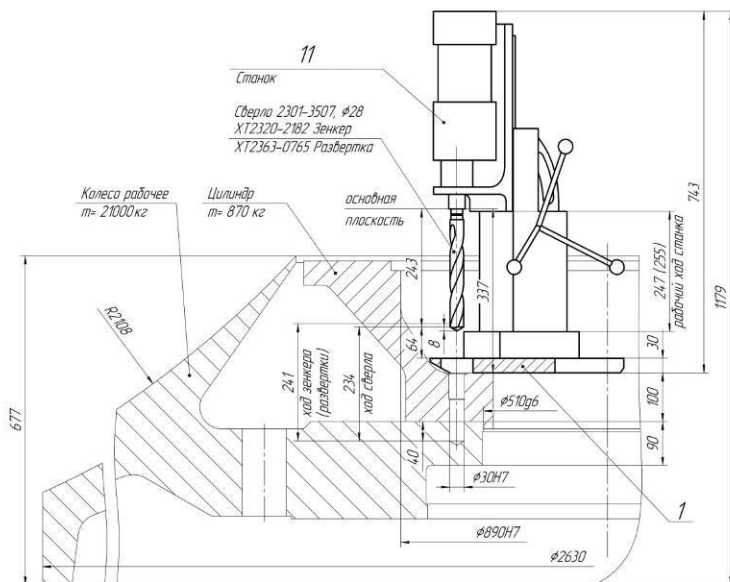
Компоновка OZCv мобильного сверлильного станка
